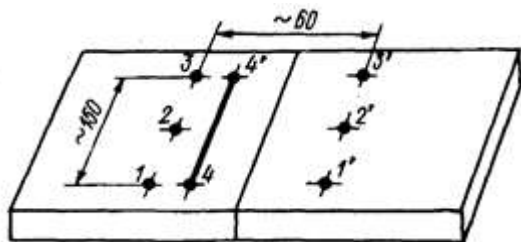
Разметка пробы перед сваркой для определения укорочения
